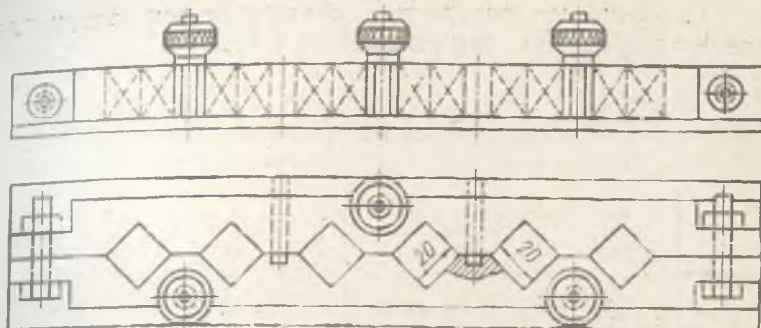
Форма для изготовления цементных образцов размером 20×20×20 мм
